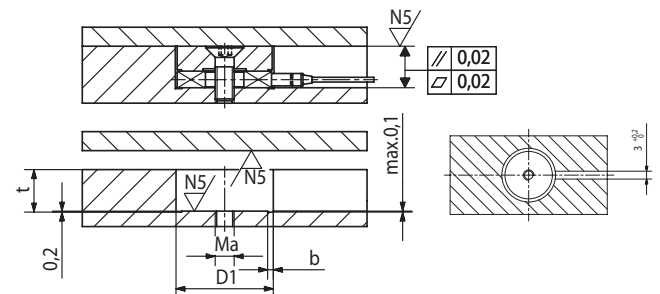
Einbau im Nebenschluss mit Vorspannscheibe
